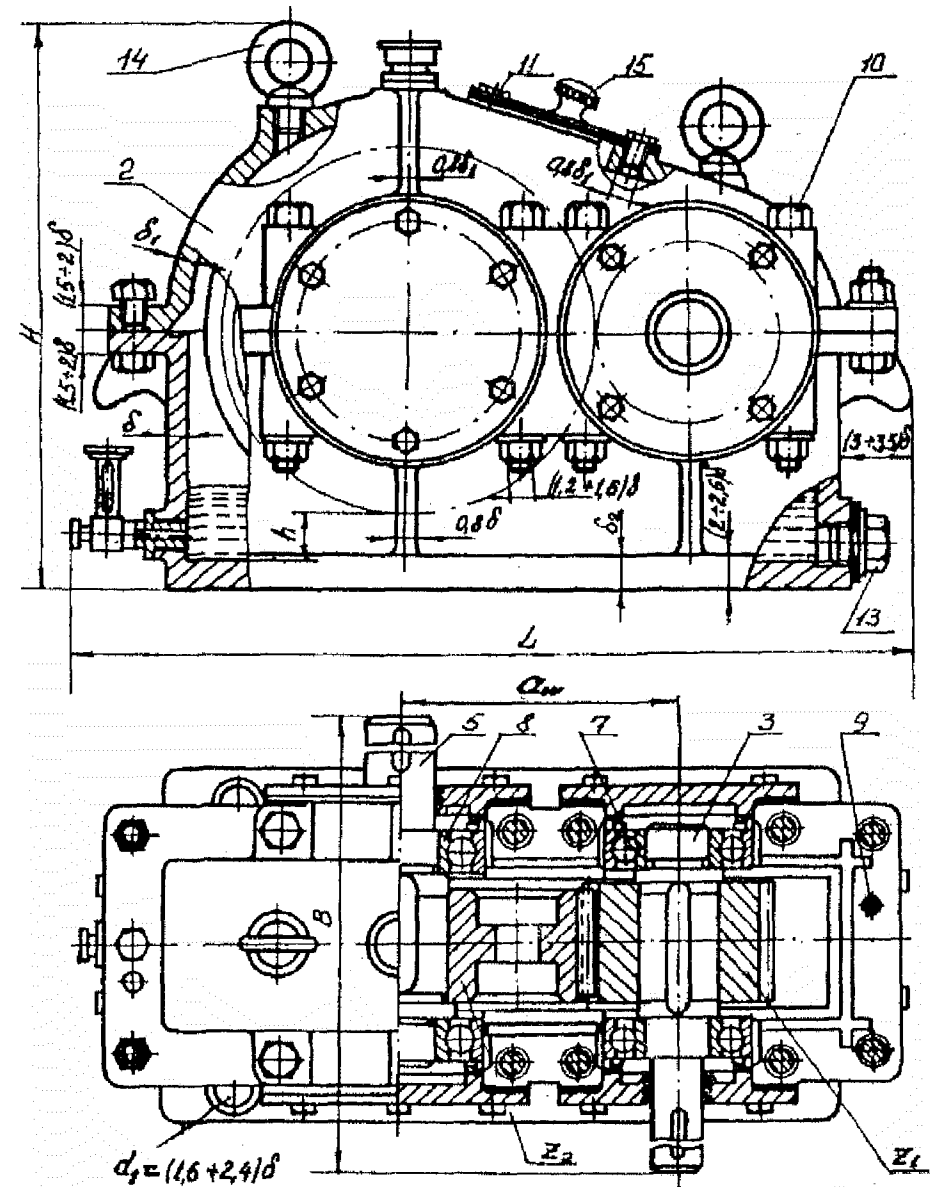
Одноступінчастий редуктор з циліндричними колесами
